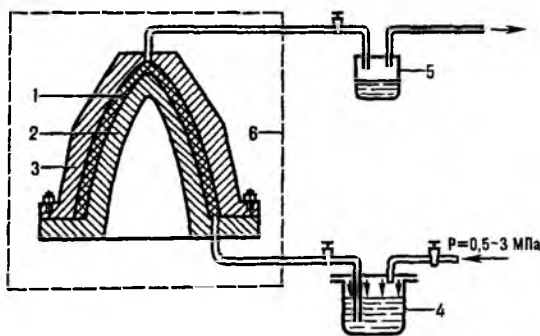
Изготовление изделий методом пропитки под давлением: 1 — заготовка изделия; 2 — пуансон; 3 — матрица; 4 — бак со связующим; 5 — лущушка; 6 — термошкаф.
